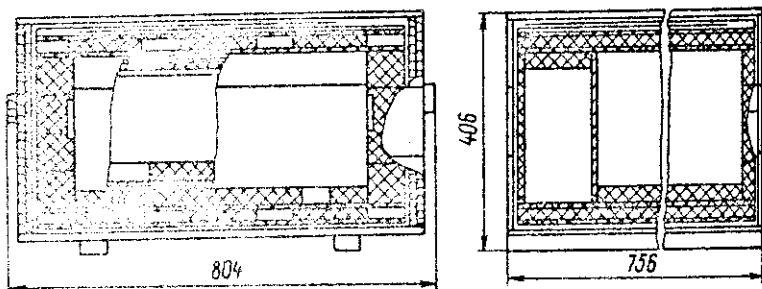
Схема транспортной упаковки блока индикаторного с УПТ и ЗИП
